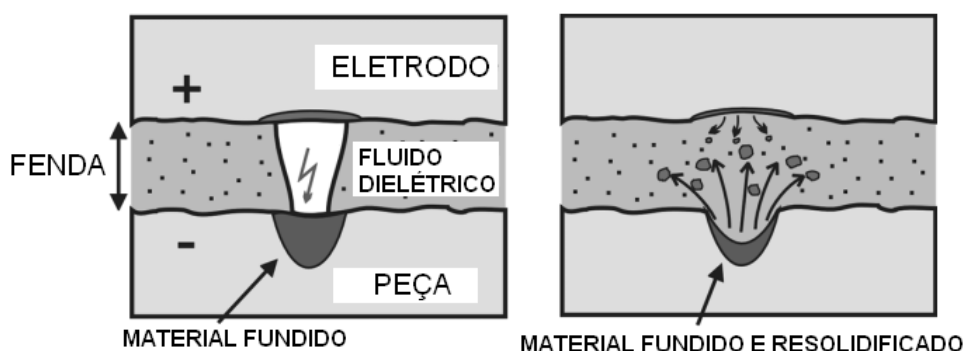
Esquemática da usinagem por descarga elétrica. (ARANTES, 2007)
